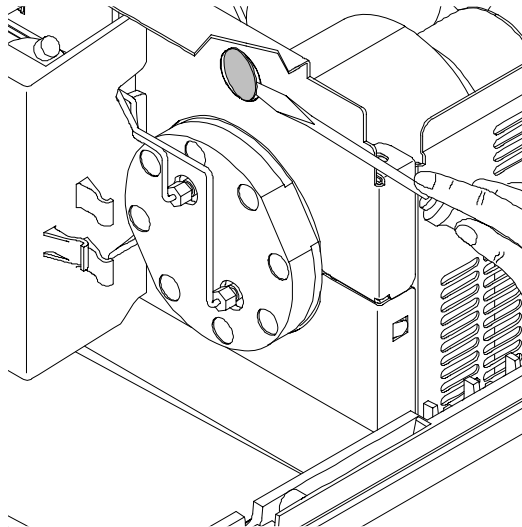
Entfernen des Metallstopfens aus dem Z-Blech
